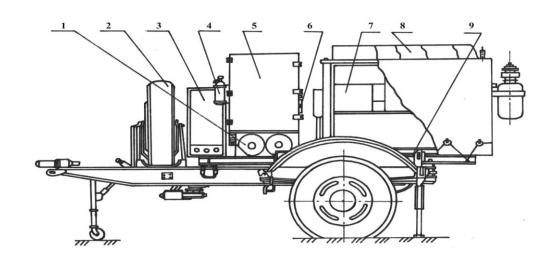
Универсальный сварочный агрегат УСА-М1.
